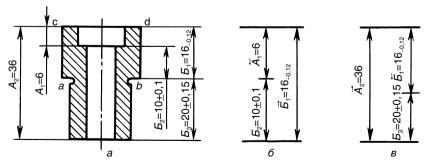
Эскиз детали и варианты схем размерных цепей
